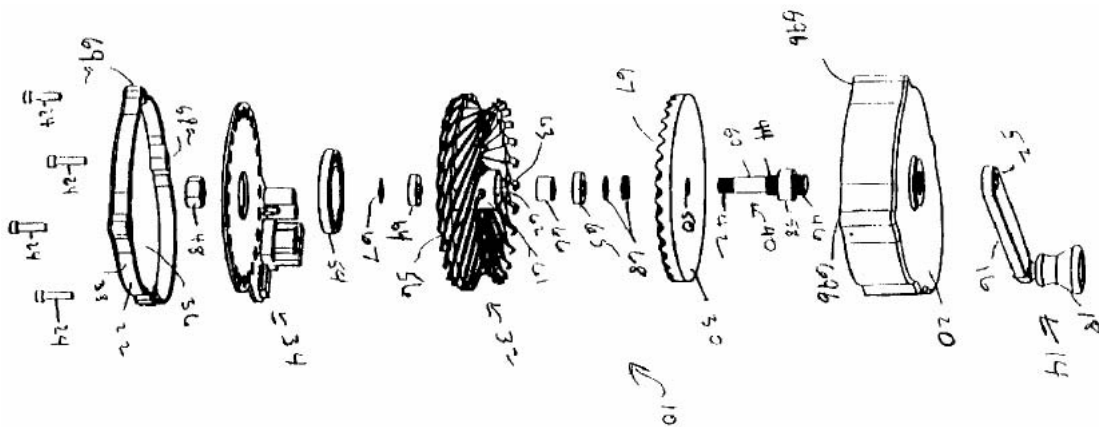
Vue éclatée du dispositif rotatif à manivelle
